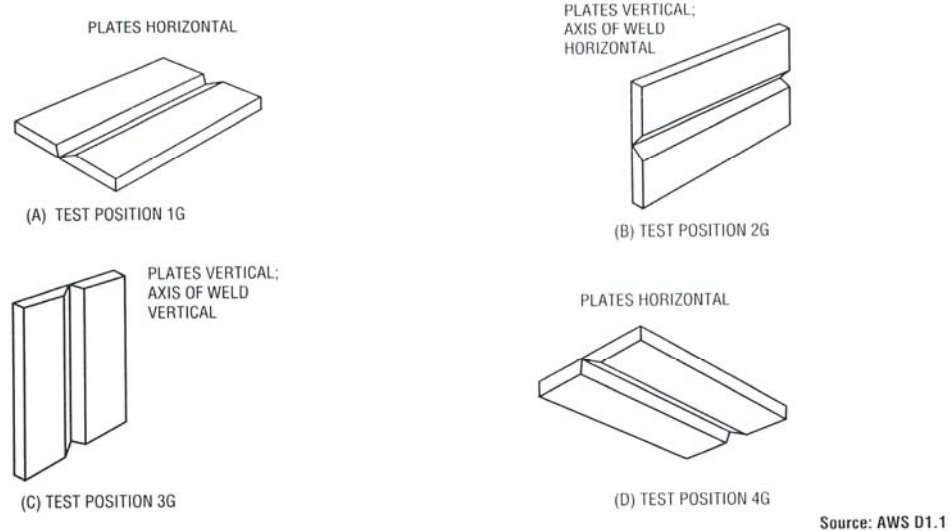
Posiciones de las planchas de prueba para soldadura de ranura.
